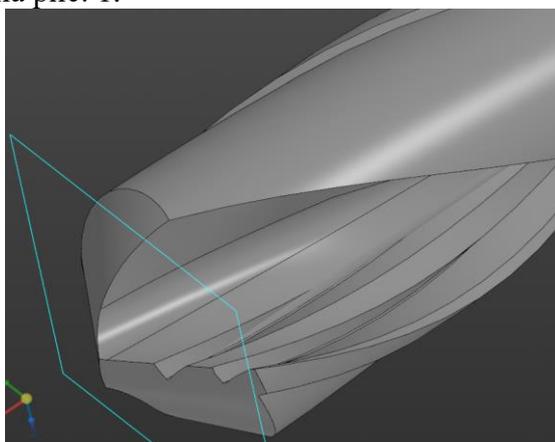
3D-модель спирального сверла со стружкоделительными канавками по передней поверхности
